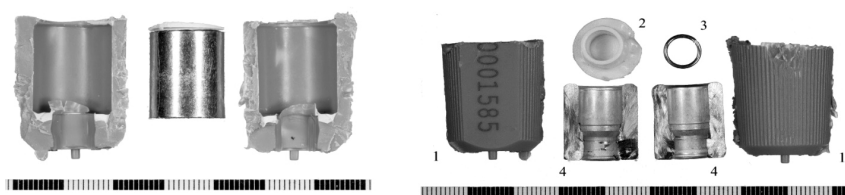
Корпус стержневого пломбировочного устройства «С-3-0421» после снятия полимерного покрытия и последующей его разборки
